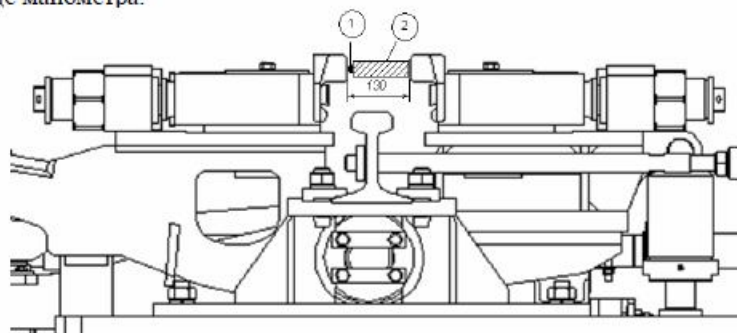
Розташування мездози на уповільнювачі: 1 – мездоза; 2 – металевий вкладиш
